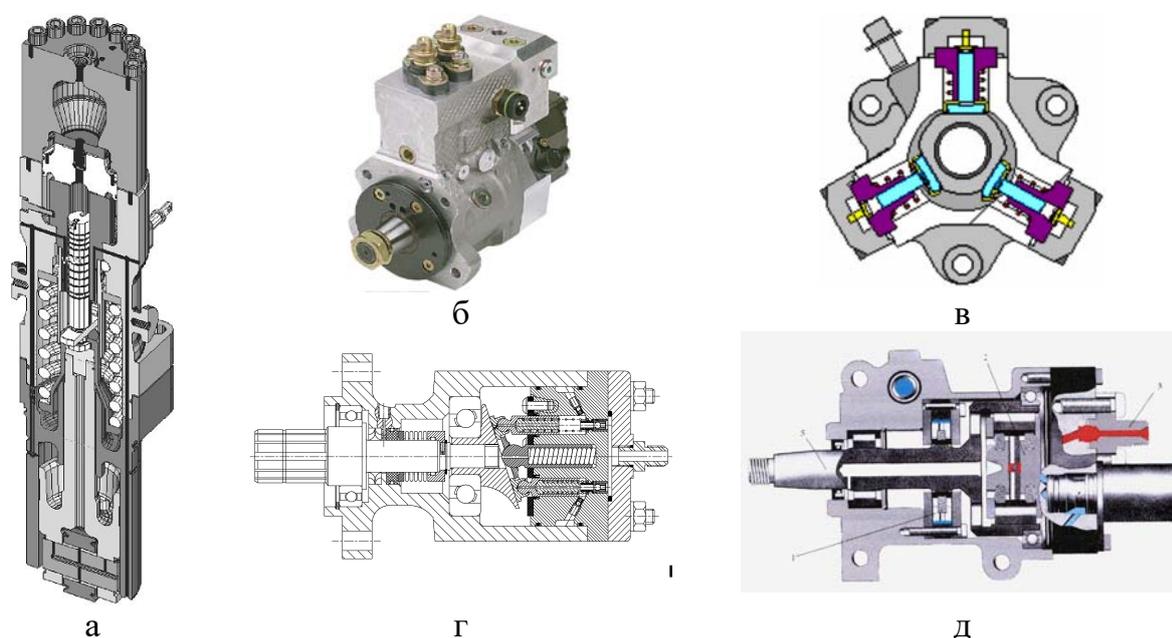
ТНВД для CR: а–индивидуальный Sulzer; б–рядный R.Bosch; в–радиально-плунжерный R.Bosch; г–аксиальный AVL; д–роторный Delphi
